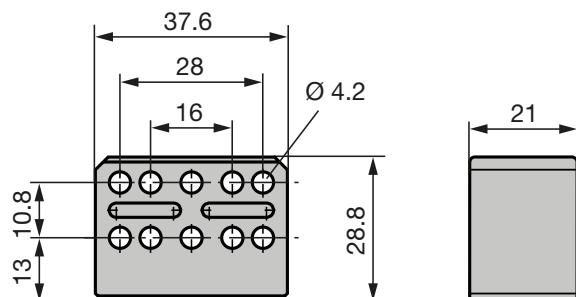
Einbaumaße Positionsgeber BTL6-A-3800-2
